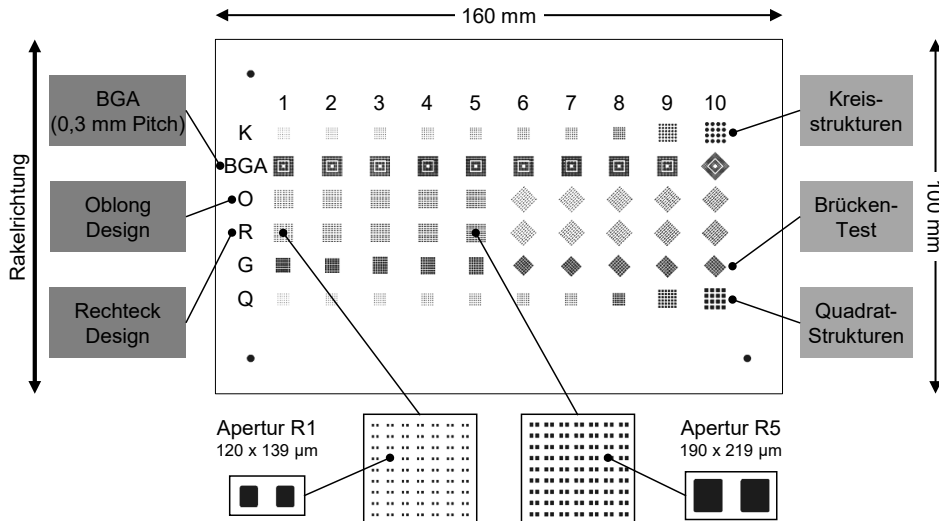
Aufbau des entwickelten Drucklayouts mit 8.000 Aperturen
